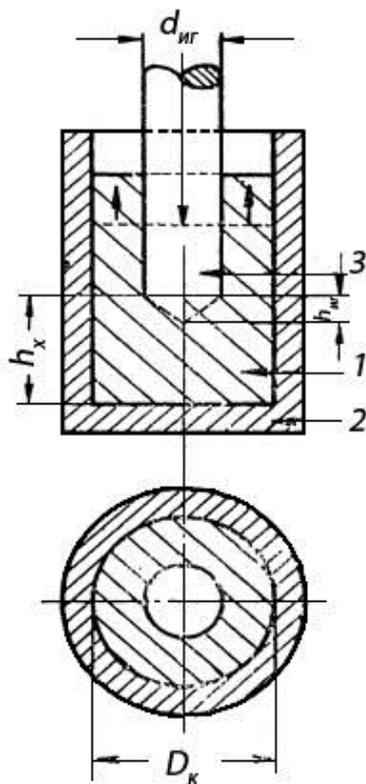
Схема закритої (наростаючої) прошивки
